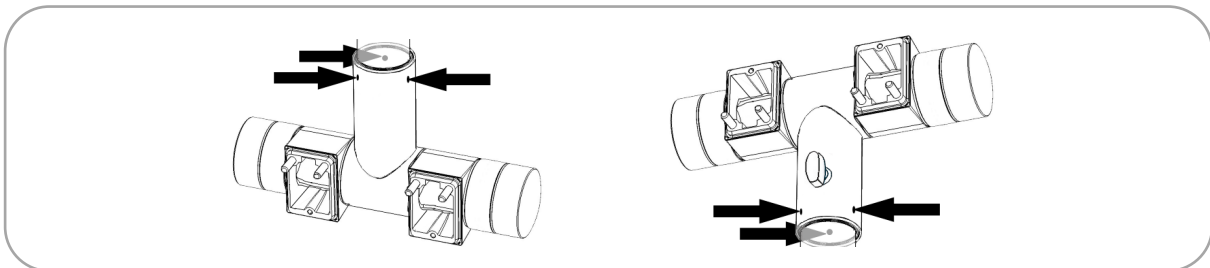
Adapter an Rohr anschrauben (links: Tragarmmontage; rechts: Standfußmontage)
